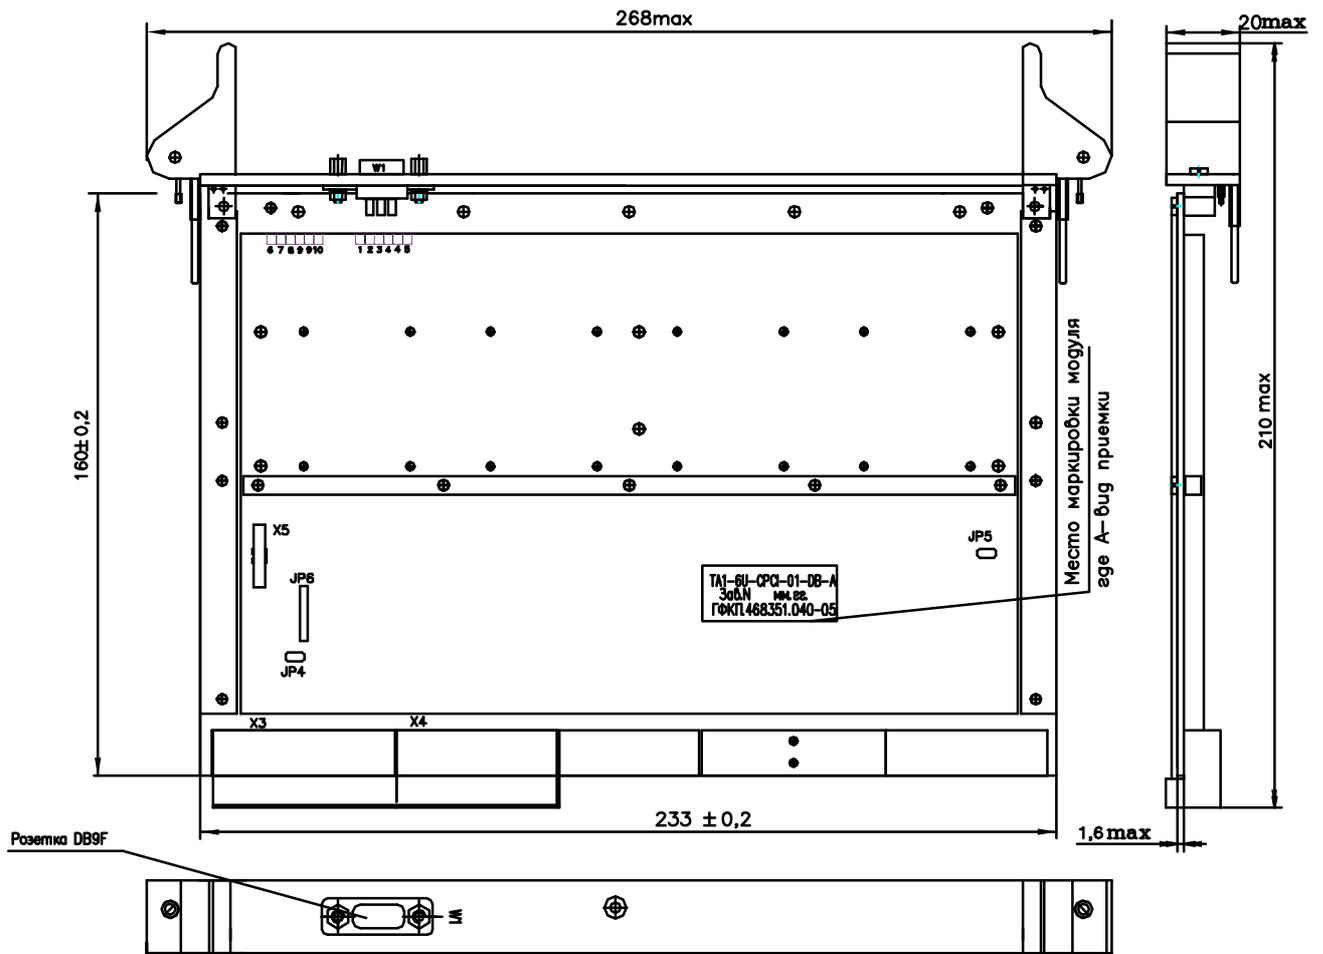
Габаритный чертеж изделия TA1-6U-CPCL-01-DB –А
